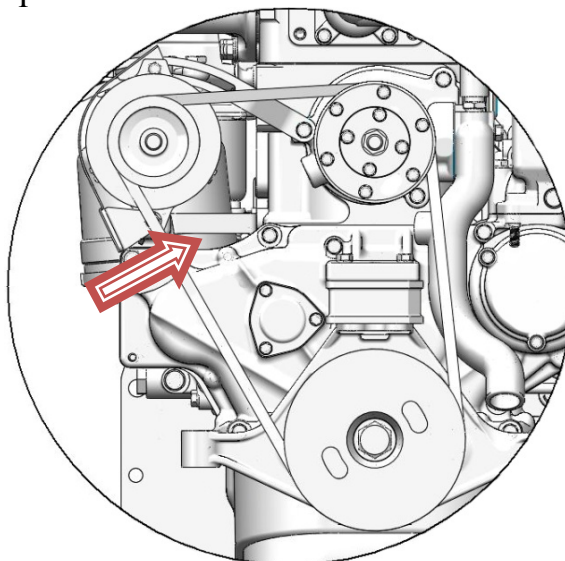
Проверка натяжения ремня вентилятора.
